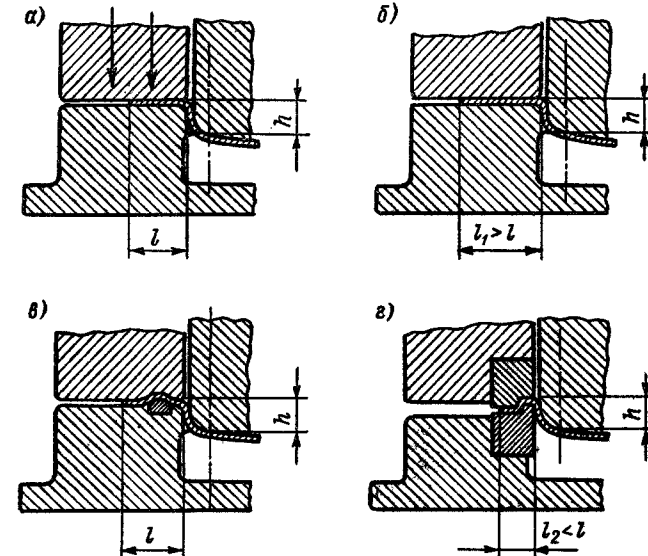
Различные способы увеличения интенсивности торможения фланца заготовки под прижимом
